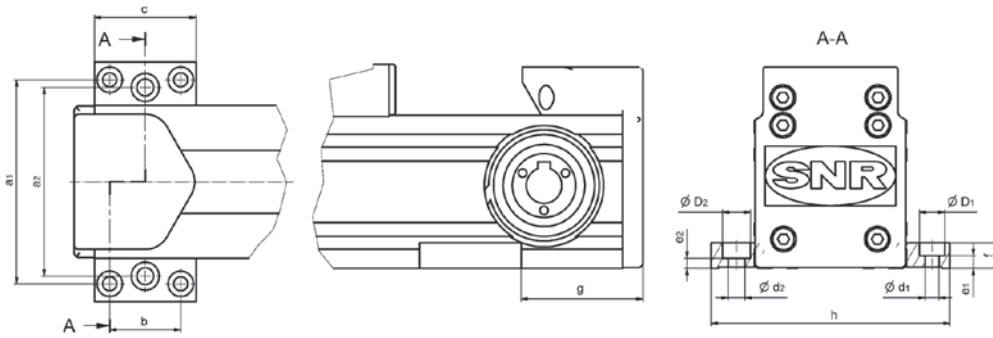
Abmessungen Befestigungsleisten AXC / AXDL
